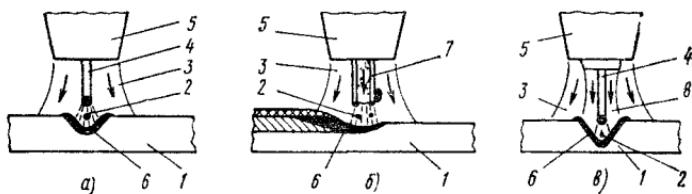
Схемы процессов сварки в СО₂.
